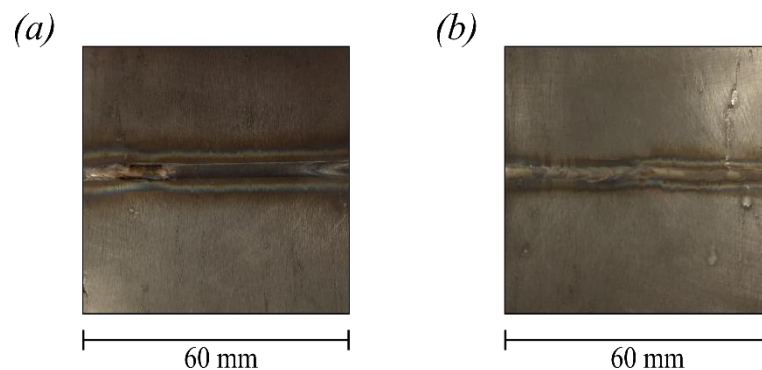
(a) Cordão soldadura na face. (b) Cordão de soldadura na raiz.
